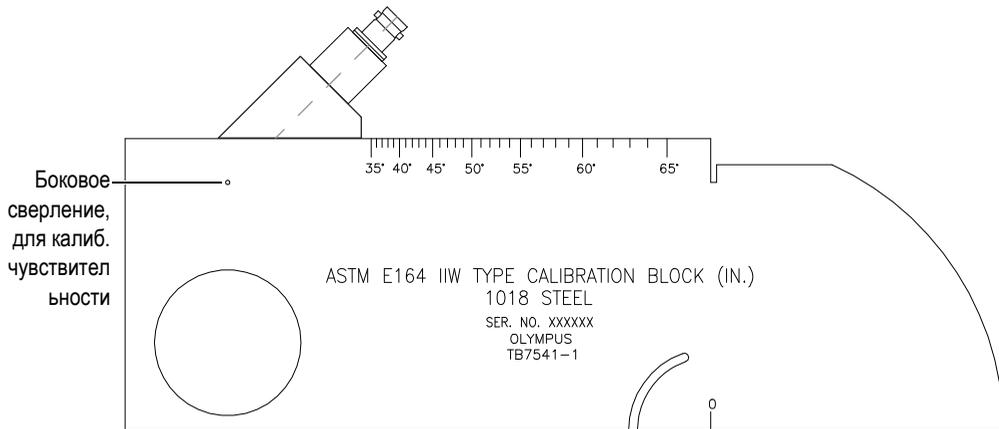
Калибровочный образец IIW и ПЭП, направленный на боковое сверление
